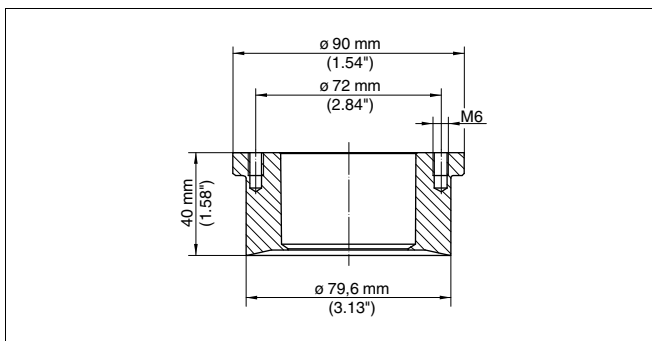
Medidas da luva soldada LA para flange tensor
